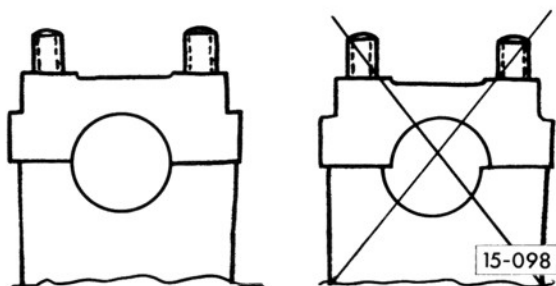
Einbaulage Lagerdeckel-Nockenwelle
